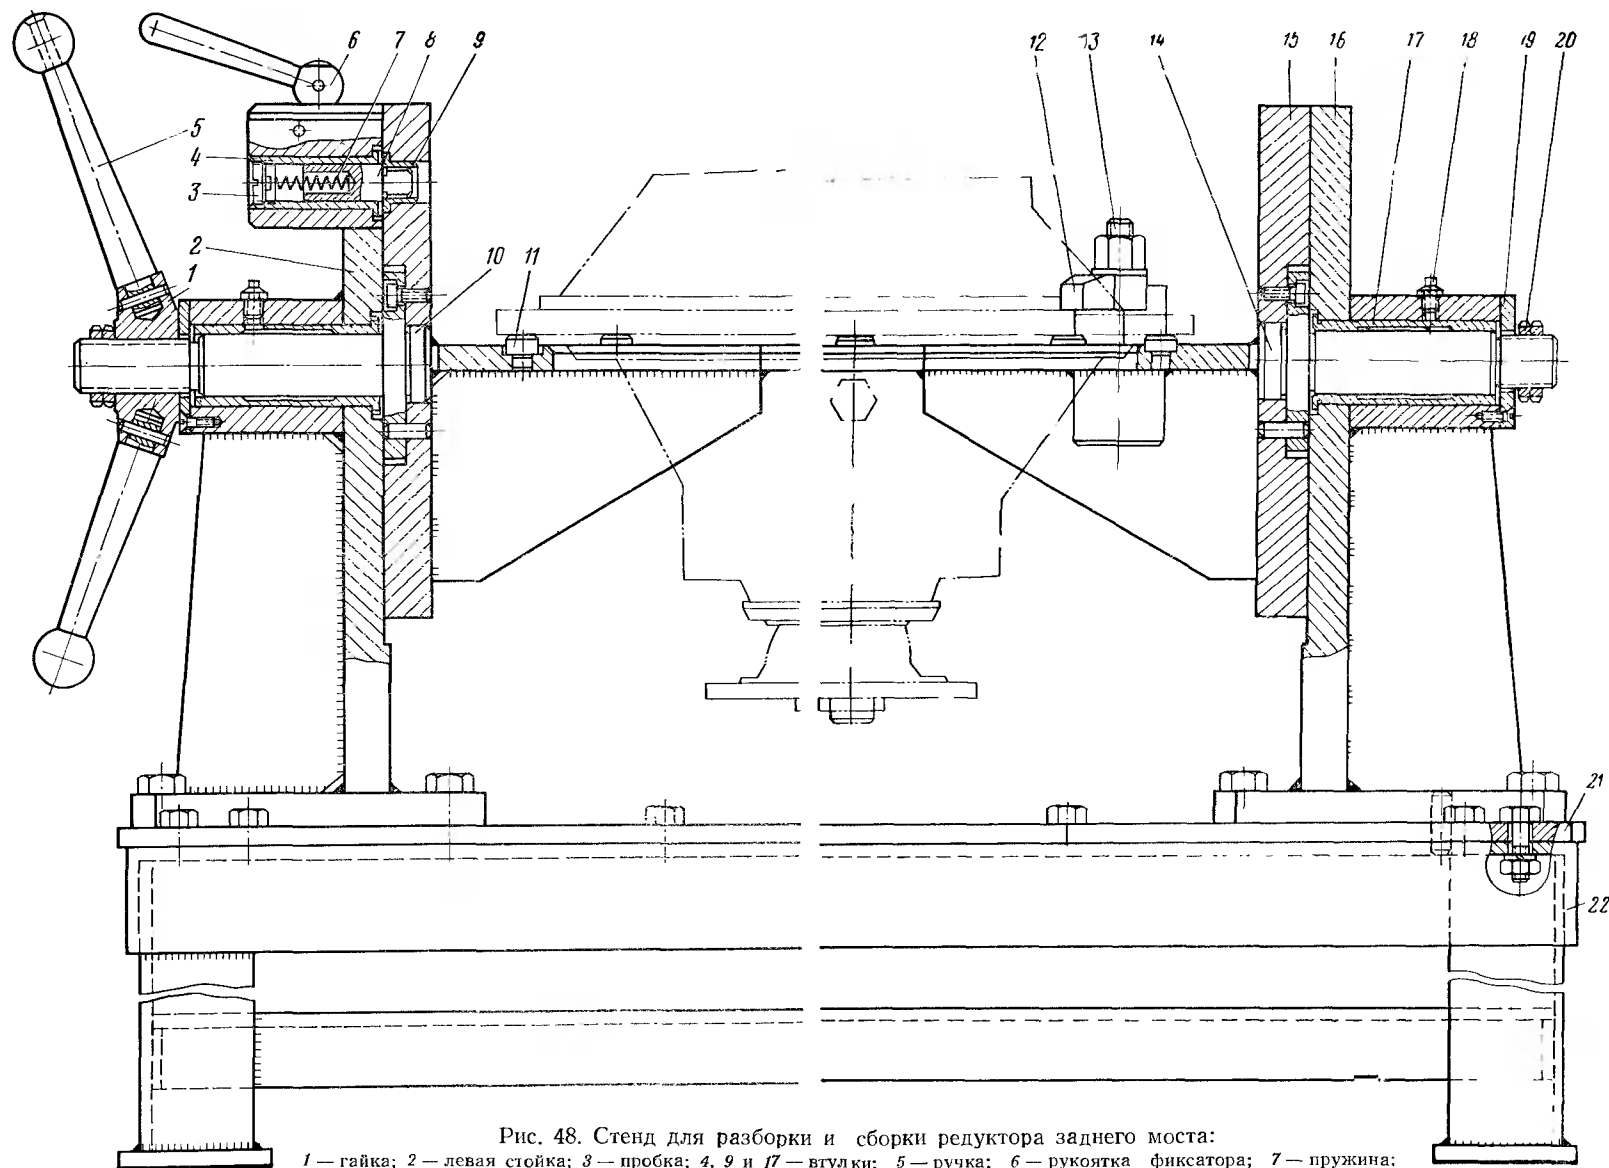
Стенд для разборки и сборки редуктора заднего моста:
